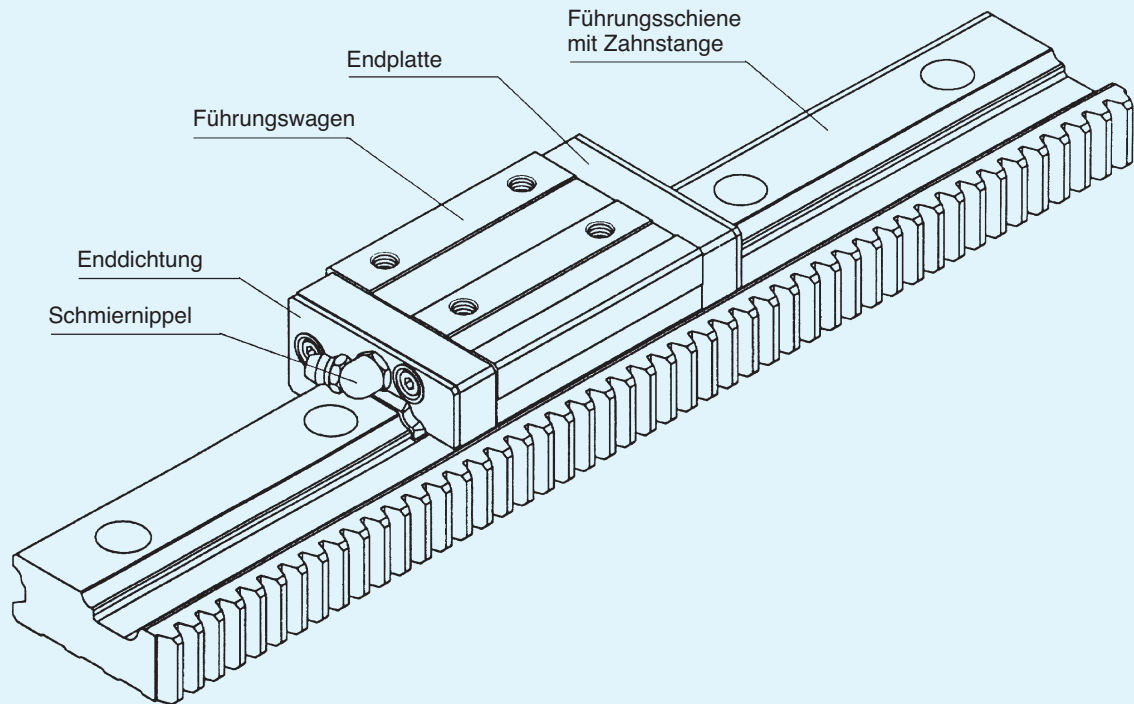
Schnittmodell der THK Linearführung GSR-R mit integrierter Zahnstange
